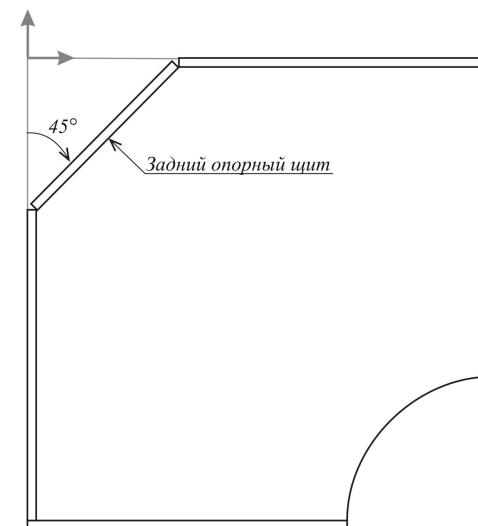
Установка и поворот заднего щита углового стола (вид сверху)
